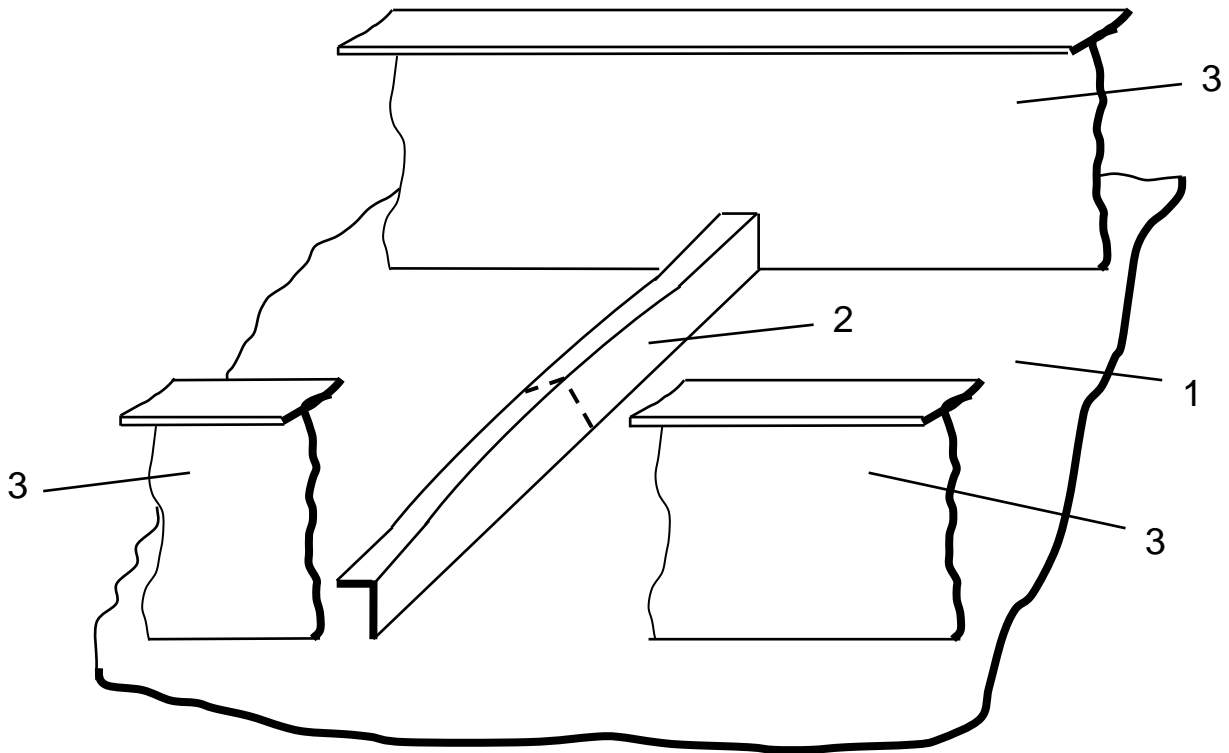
Вариант предлагаемого перекрытия с предварительным наклоном холостой балки в сторону полки, получаемого путем силового воздействия после установки и крепления балки нормально к обшивке
